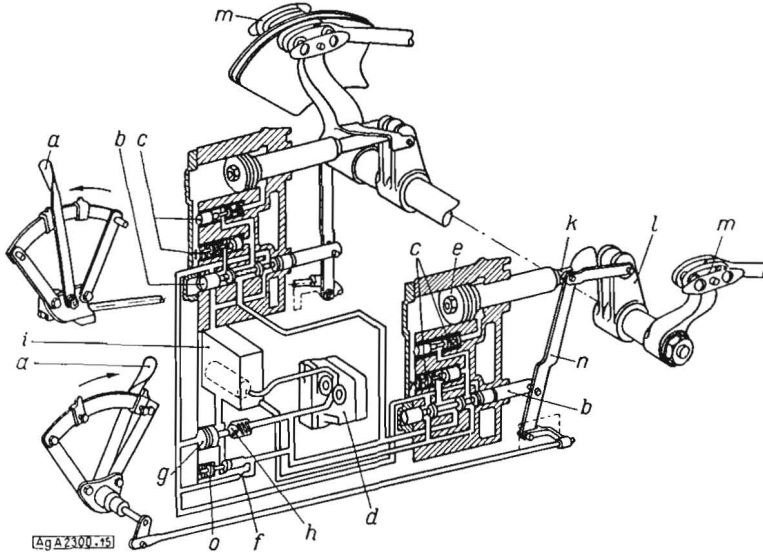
(links). Feinststeuerungshydraulik der JHC (Farmall A)
